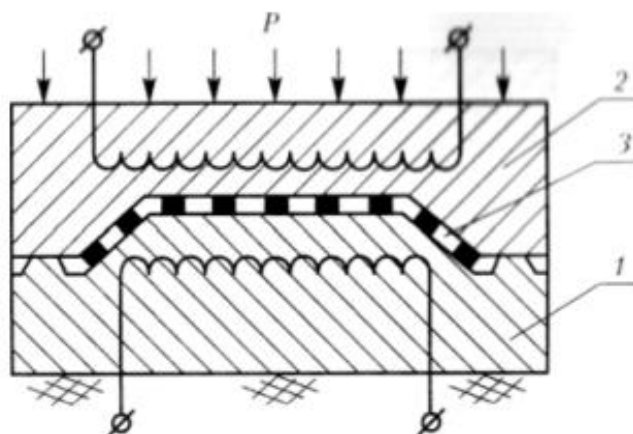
формование прямым прессованием: 1,2 – нижняя и верхняя части пресс формы, 3 – листовой формовочный материал
